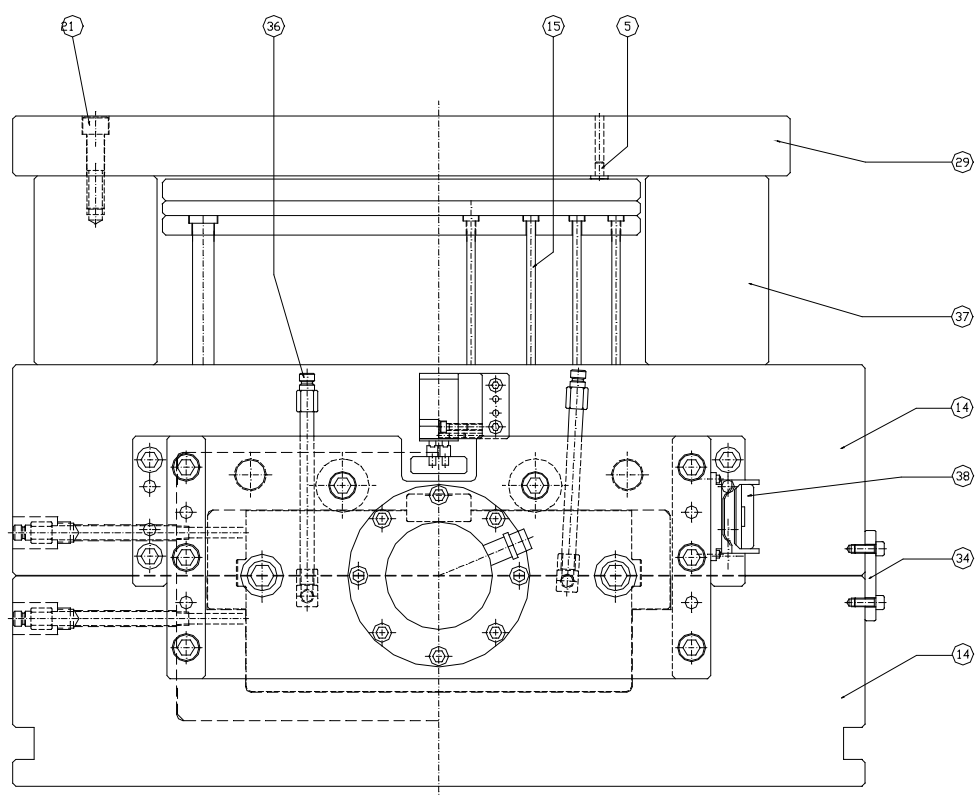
Desenho de conjunto do molde (vista de cima) (4)
